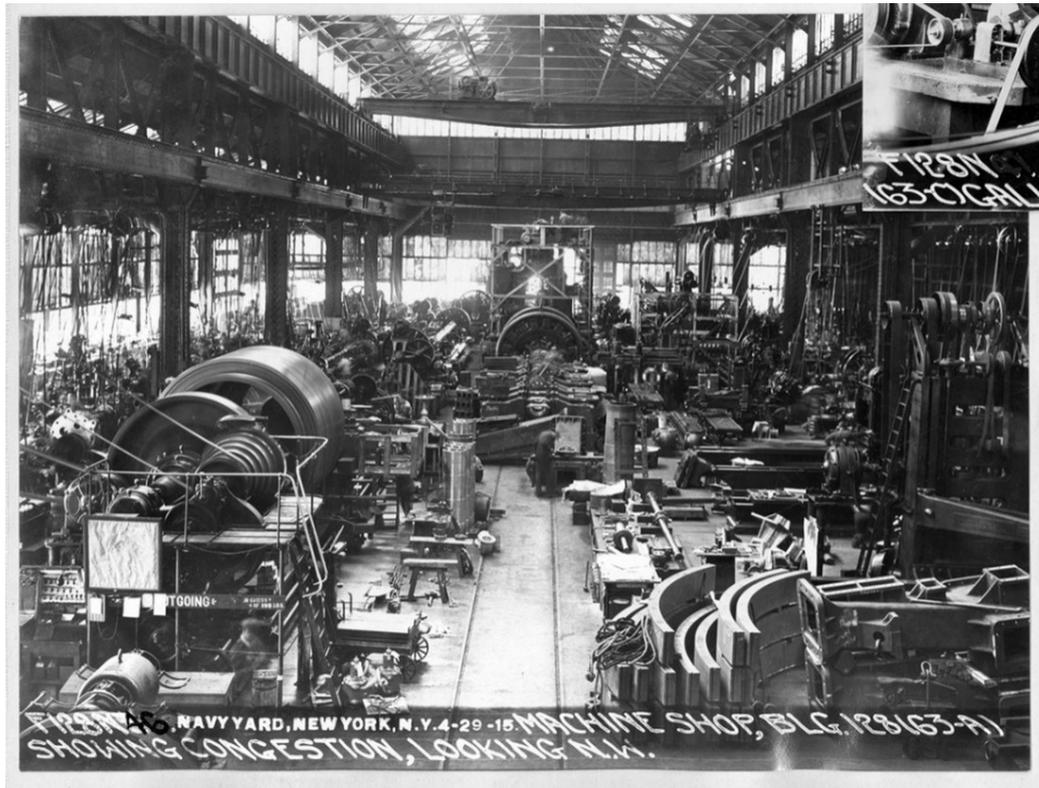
Building 128, Innenperspektive der Halle⁷⁷
